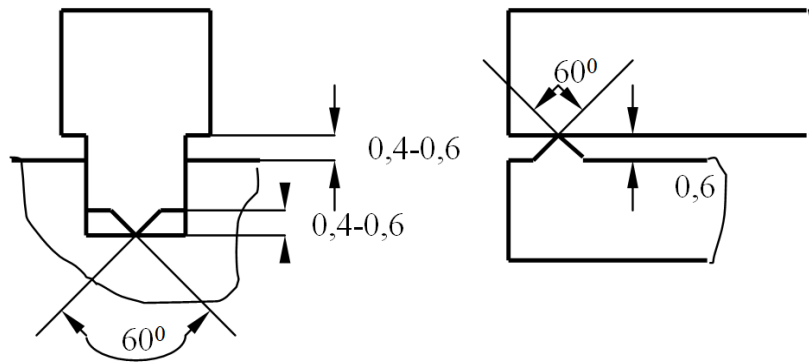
Стыки деталей из термопластов, подготовленных под ультразвуковую сварку
